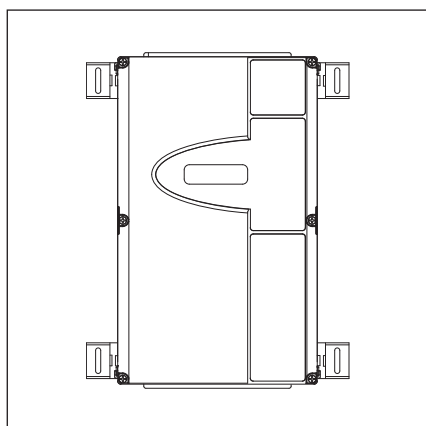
Корпус блока управления с горизонтально закрепленными монтажными опорами
